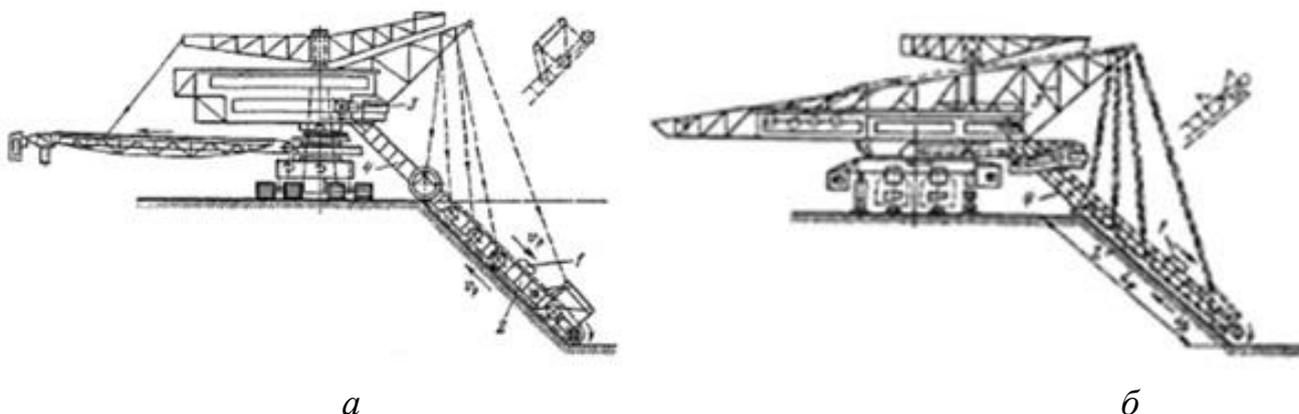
Конструктивные схемы многоковшовых экскаваторов:
